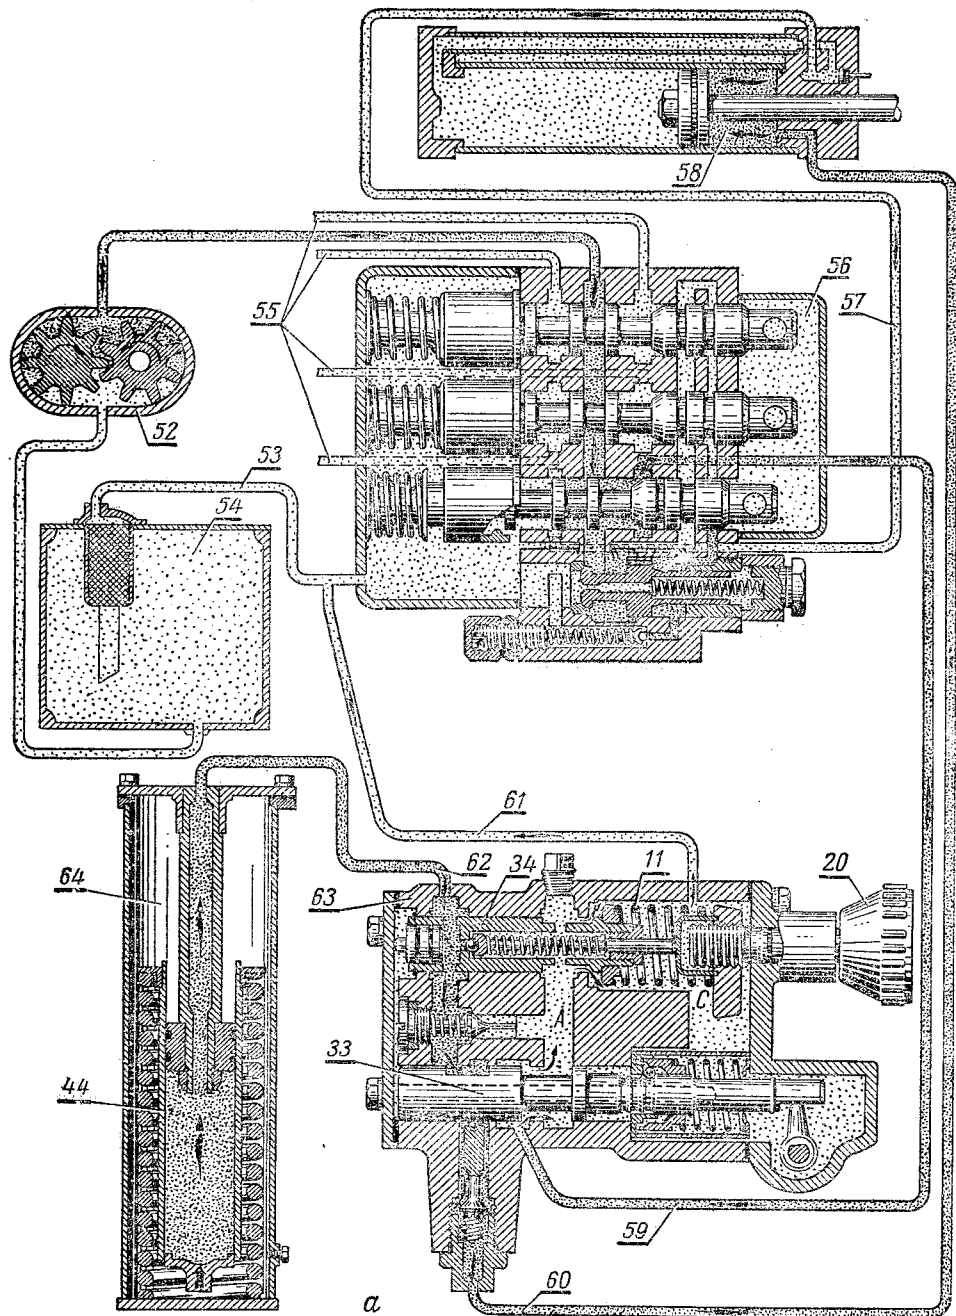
Схема работы гидроувеличителя сцепного веса.
